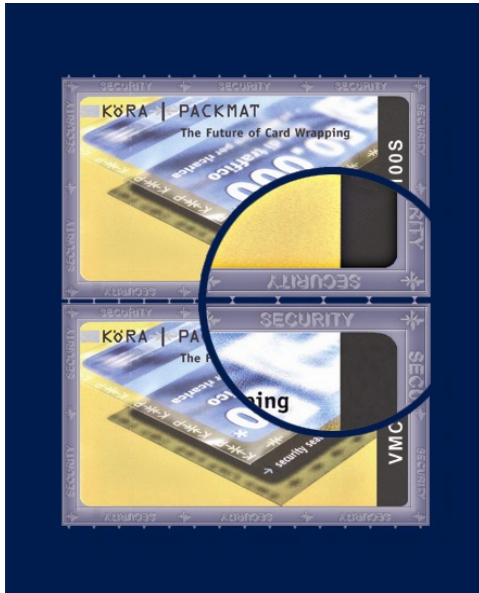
Beispiel für eine Ultraschallschweißnaht
